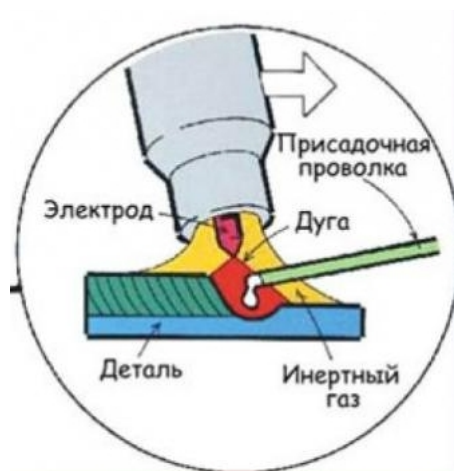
Схема аргонодуговой сварки неплавящимся электродом
